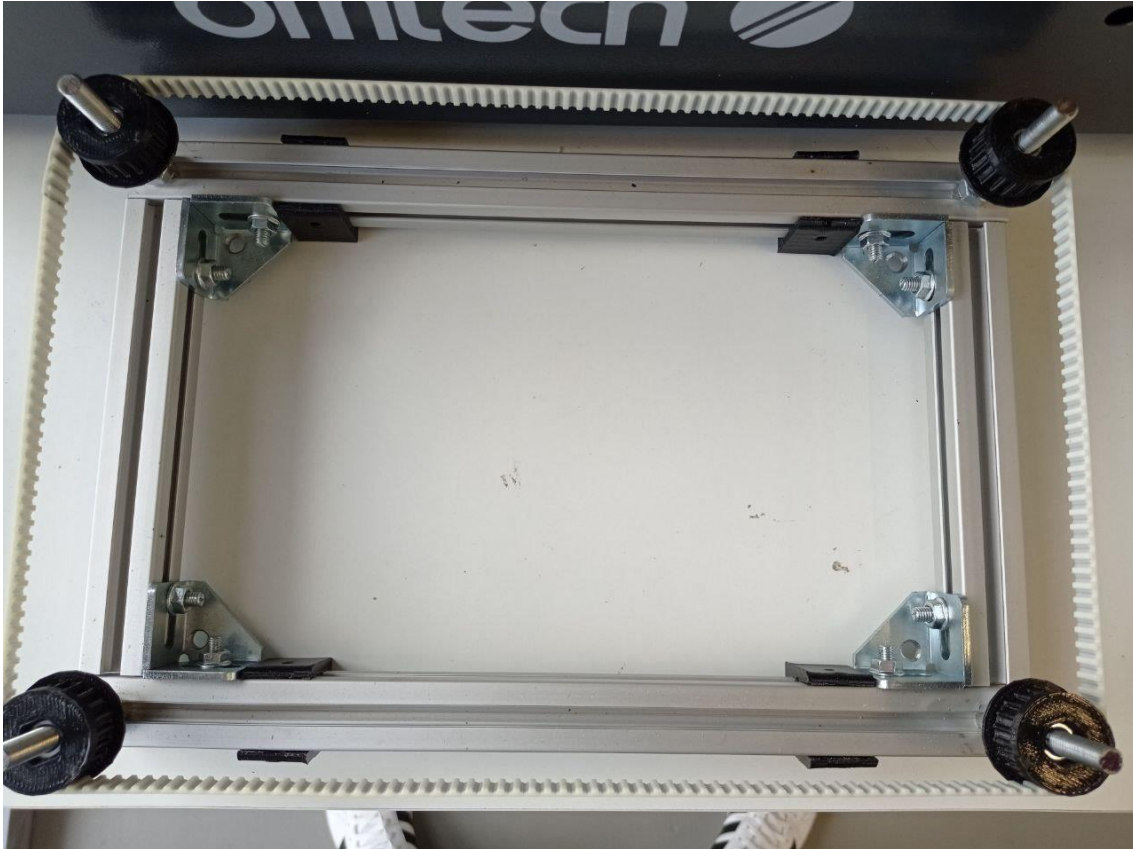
Mecanismo de la cama elevable [Imagen propia]
